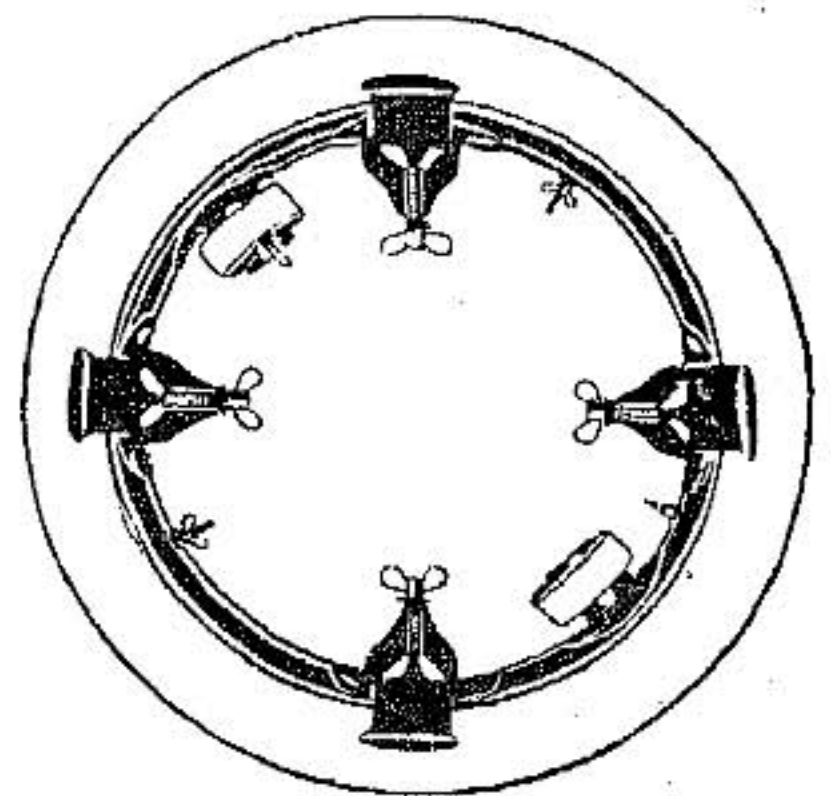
Запасный ободъ Степней (для двухъ размѣровъ колеса).
